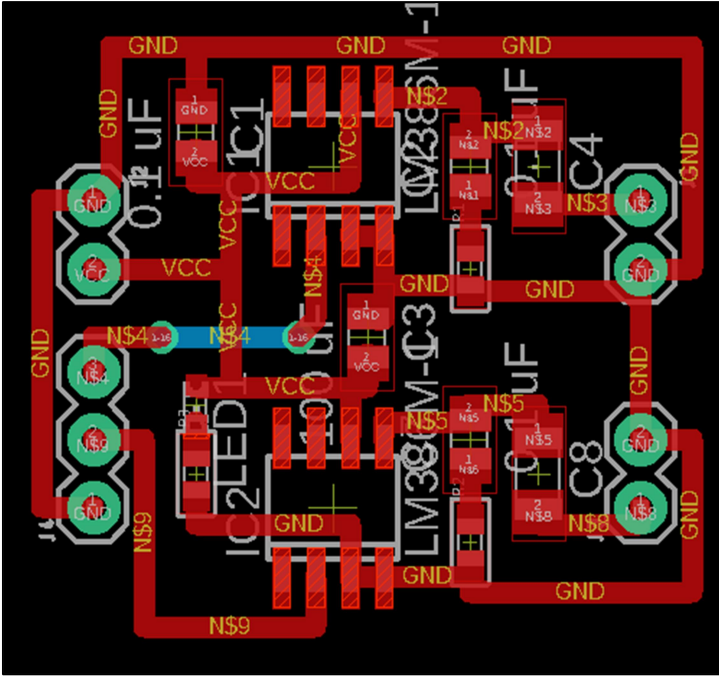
Dessin avant projet du circuit imprimé dans EAGLE.
